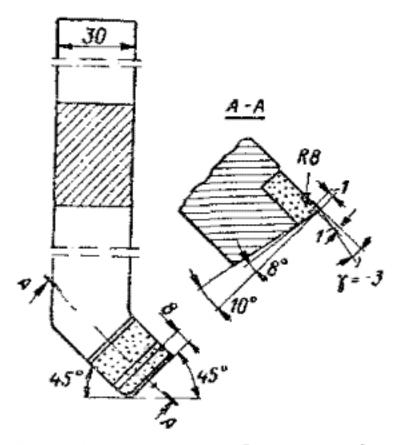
Проходной черновой резец строгальщика Ю. Н. Мотакова.
